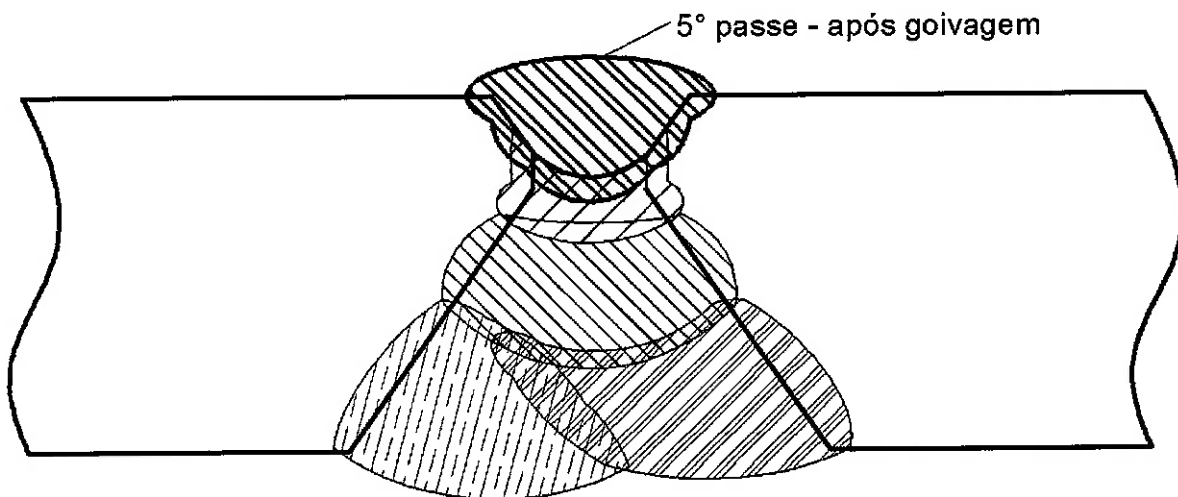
Passe de raiz da junta soldada.
